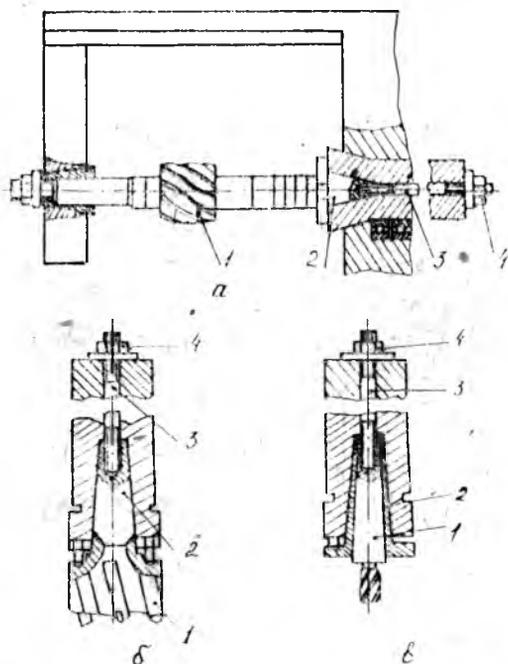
Установка и крепление фрез: а — на горизонтальном шпинделе; б, в — на вертикальном шпинделе поворотной головки
